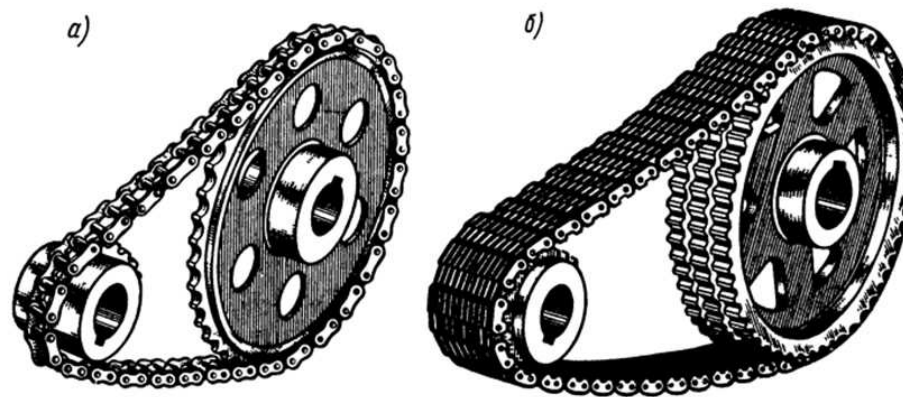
Цепная передача: *а* — роликовой цепью; *б* — зубчатой цепью
